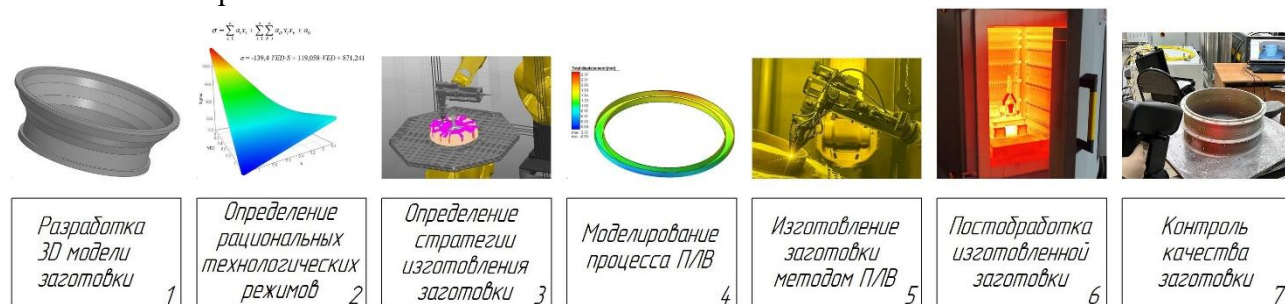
Основные этапы изготовления заготовок по технологии ПЛВ
